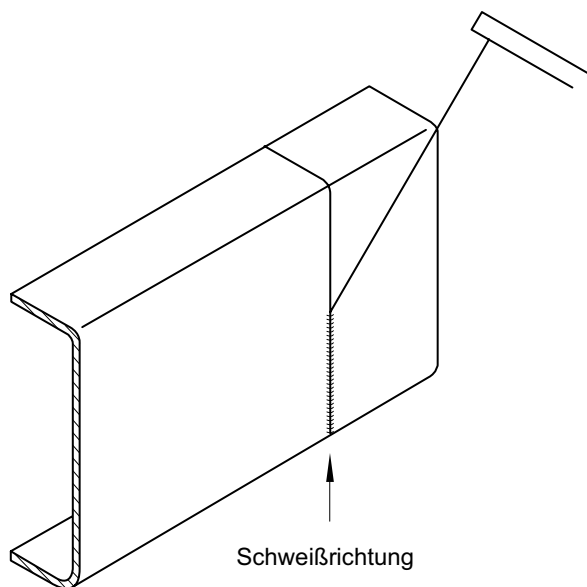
Senkrechte Rahmenschweißung ESC-090
